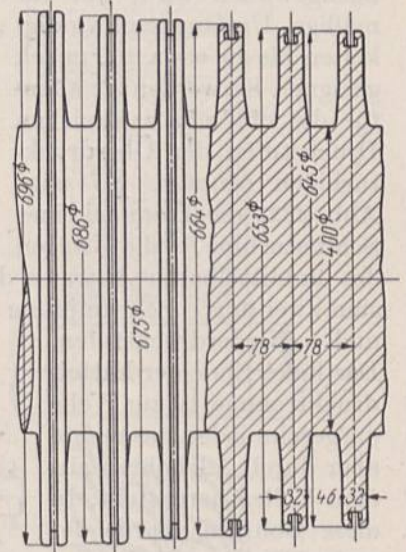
Mit der Welle aus einem Stück gedrehter Läufer, AEG, Berlin. M. 1:10.
